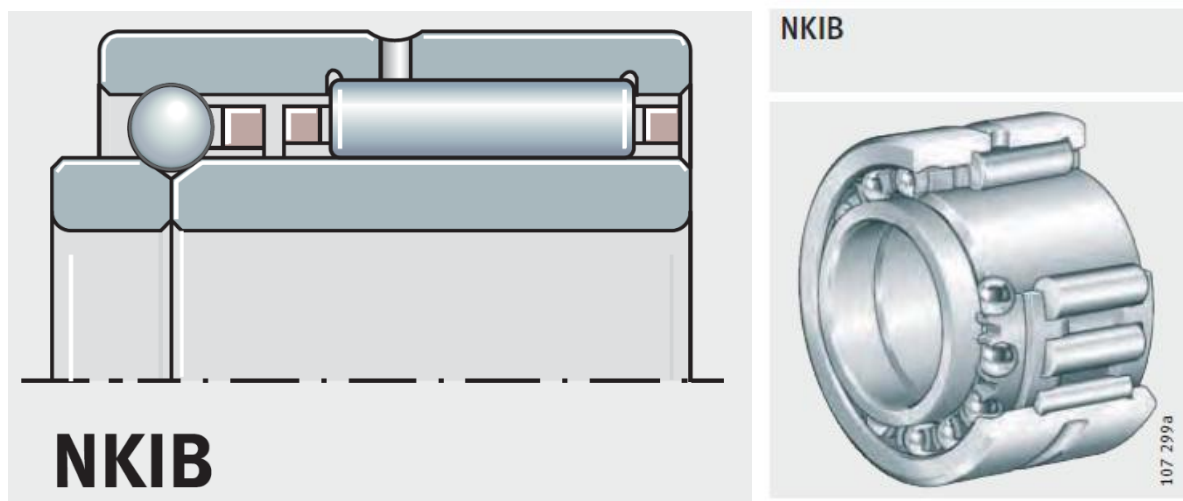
Конструкция подшипника серии NKIB ф INA
